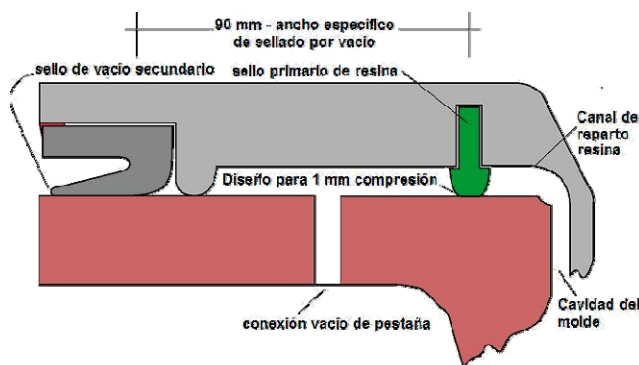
Sección de un molde de RTM-Light y forma de llenado del interior del molde.
